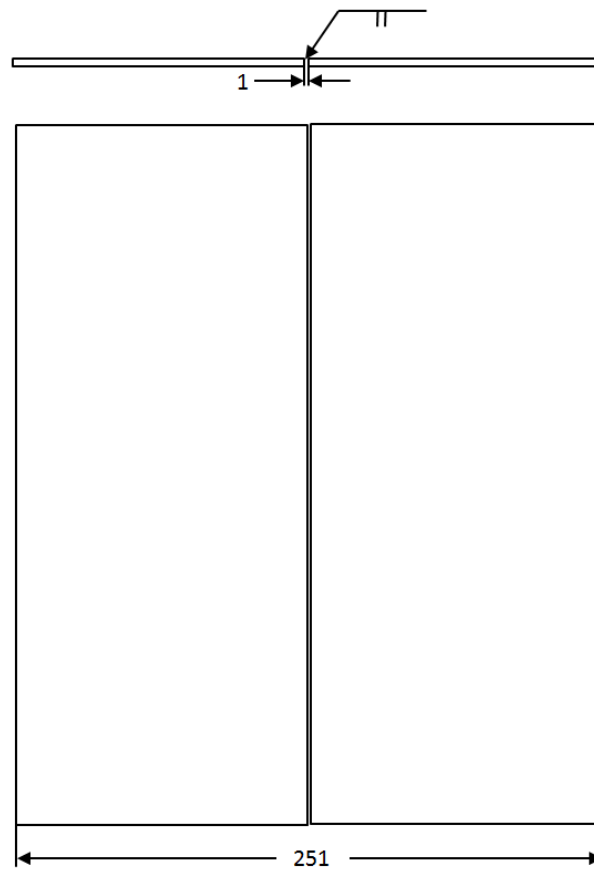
Disposição dos corpos de prova para soldagem.
